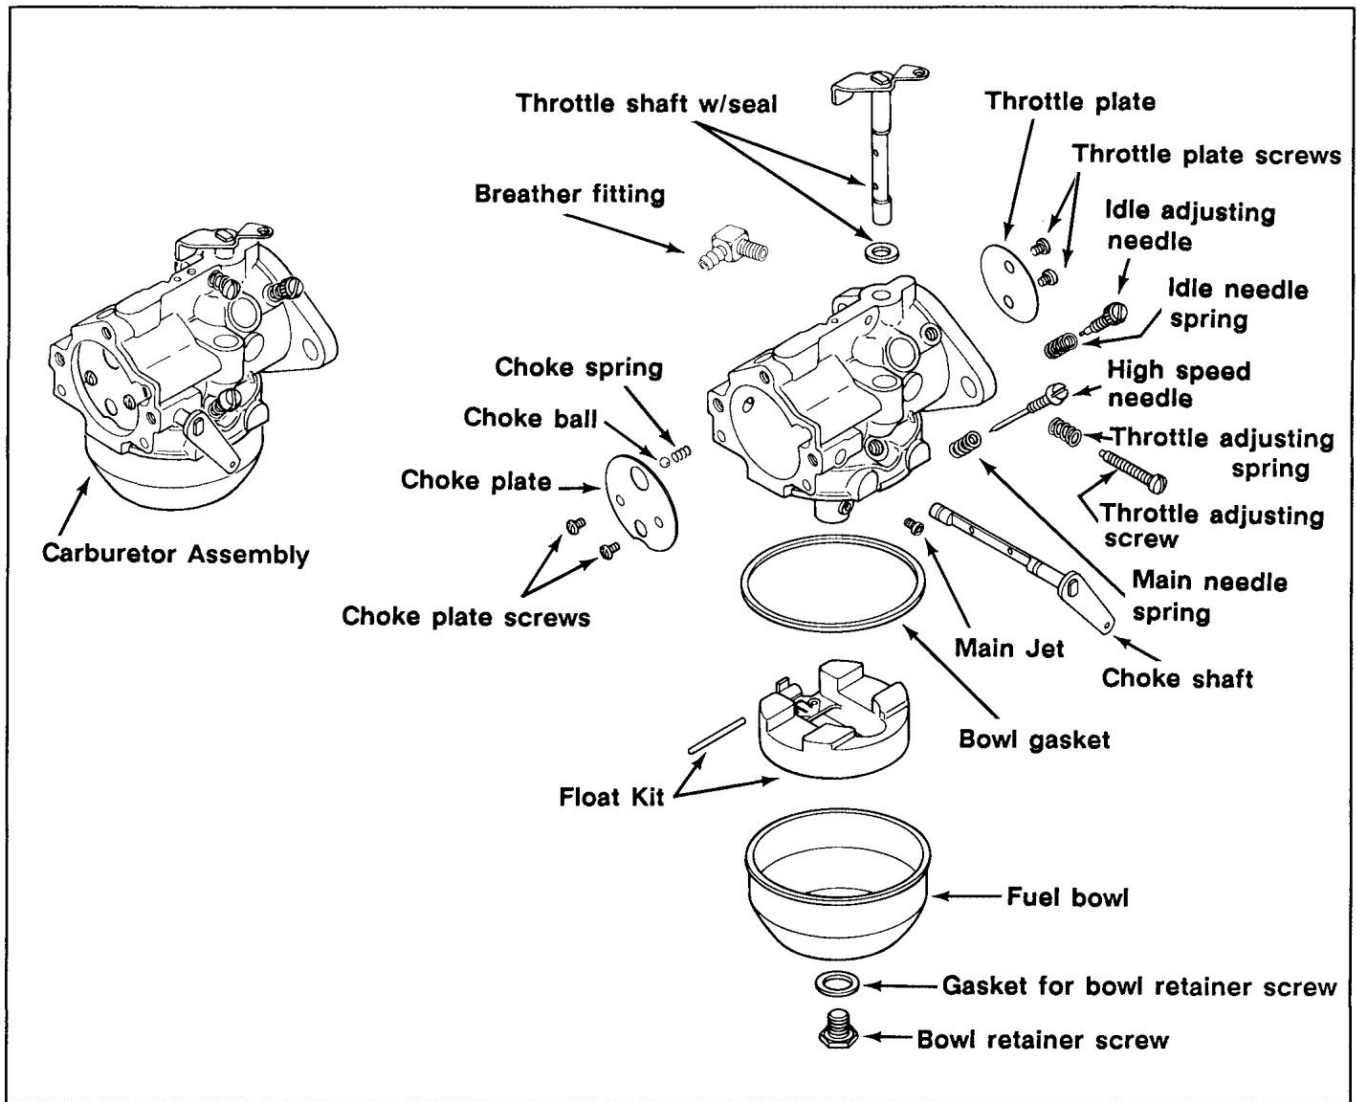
Carburateur à jet fixe/réglable Walbro - Vue éclatée
